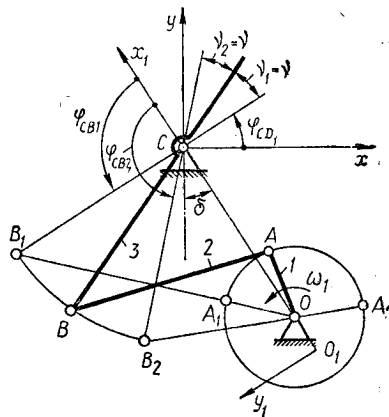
Шарнирный четырехзвенный механизм манипулятора
